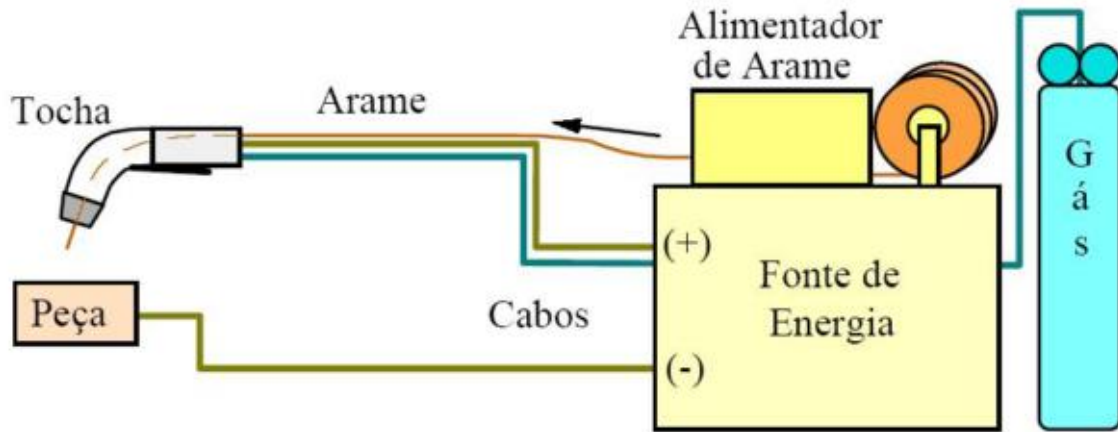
Equipamento básico para a soldagem GMAW (Dobignies, 2008).
